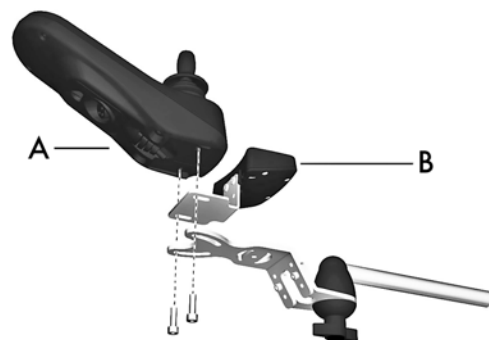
Das Steuerpult ist mit zwei Schrauben auf dem drehbaren Pulthalter befestigt.
